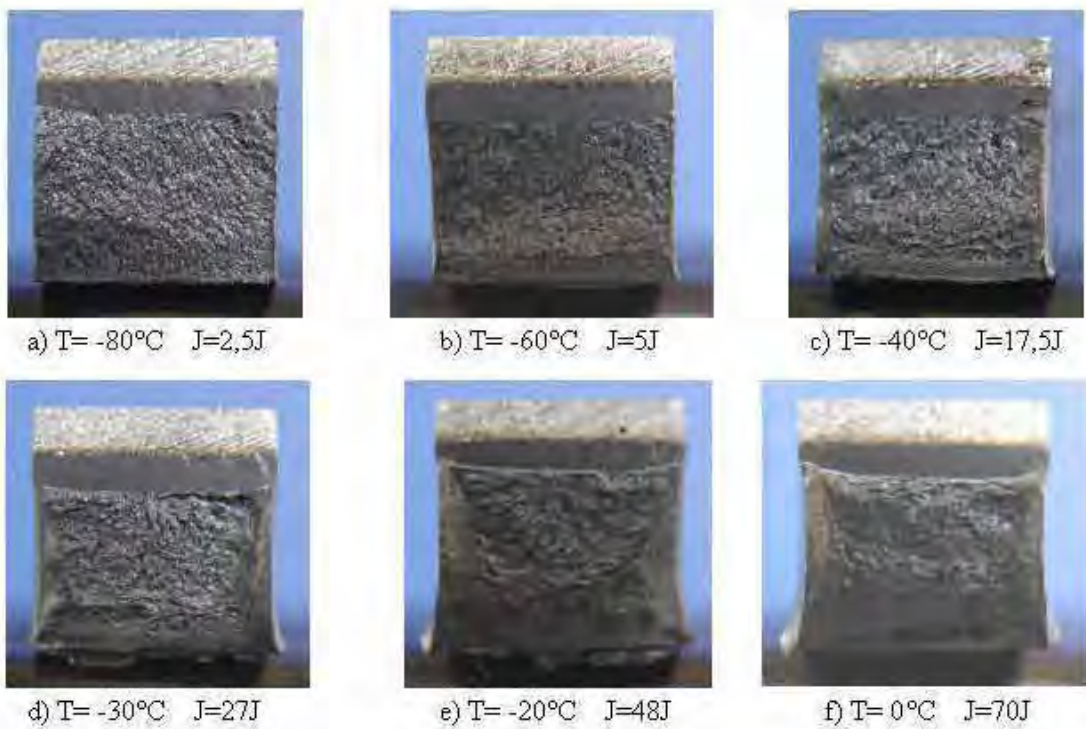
Fractografia da superfície de fratura do aço A516 - CF, corpo-de-prova pré-trincado.
